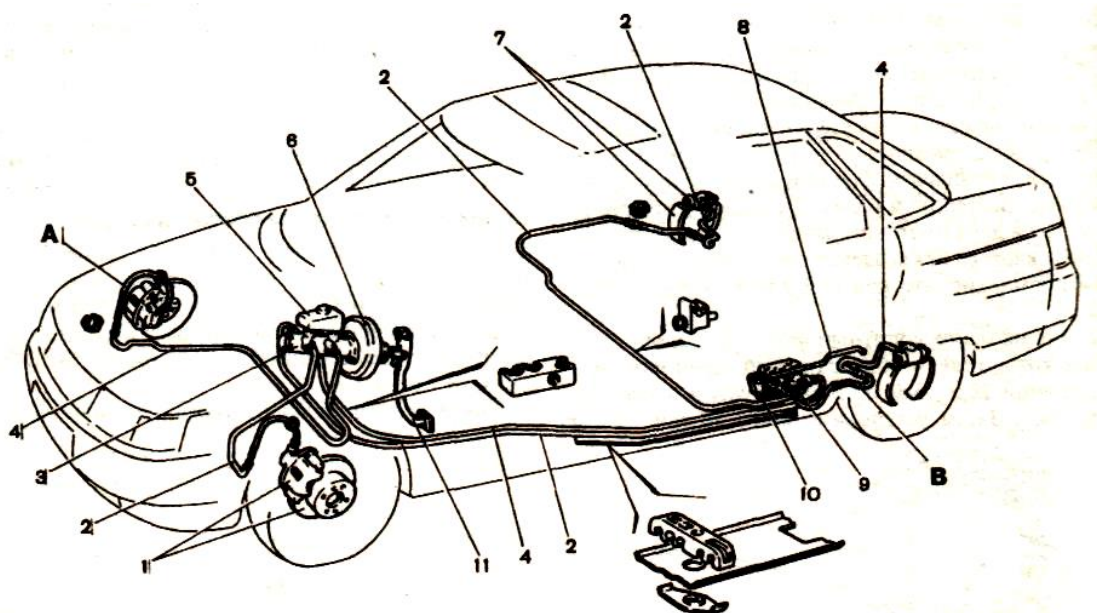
Схема гидропривода тормозов автомобиля ВАЗ-2110
